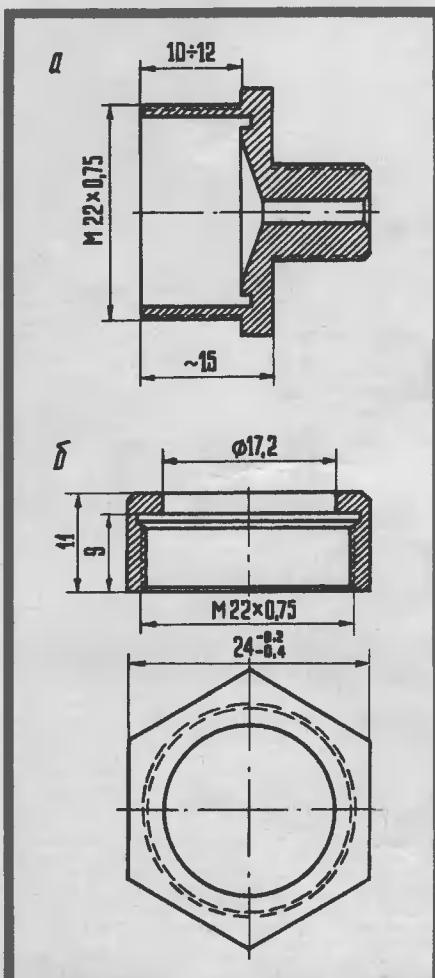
Детали включателя: а — корпус; б — накидная гайка.
